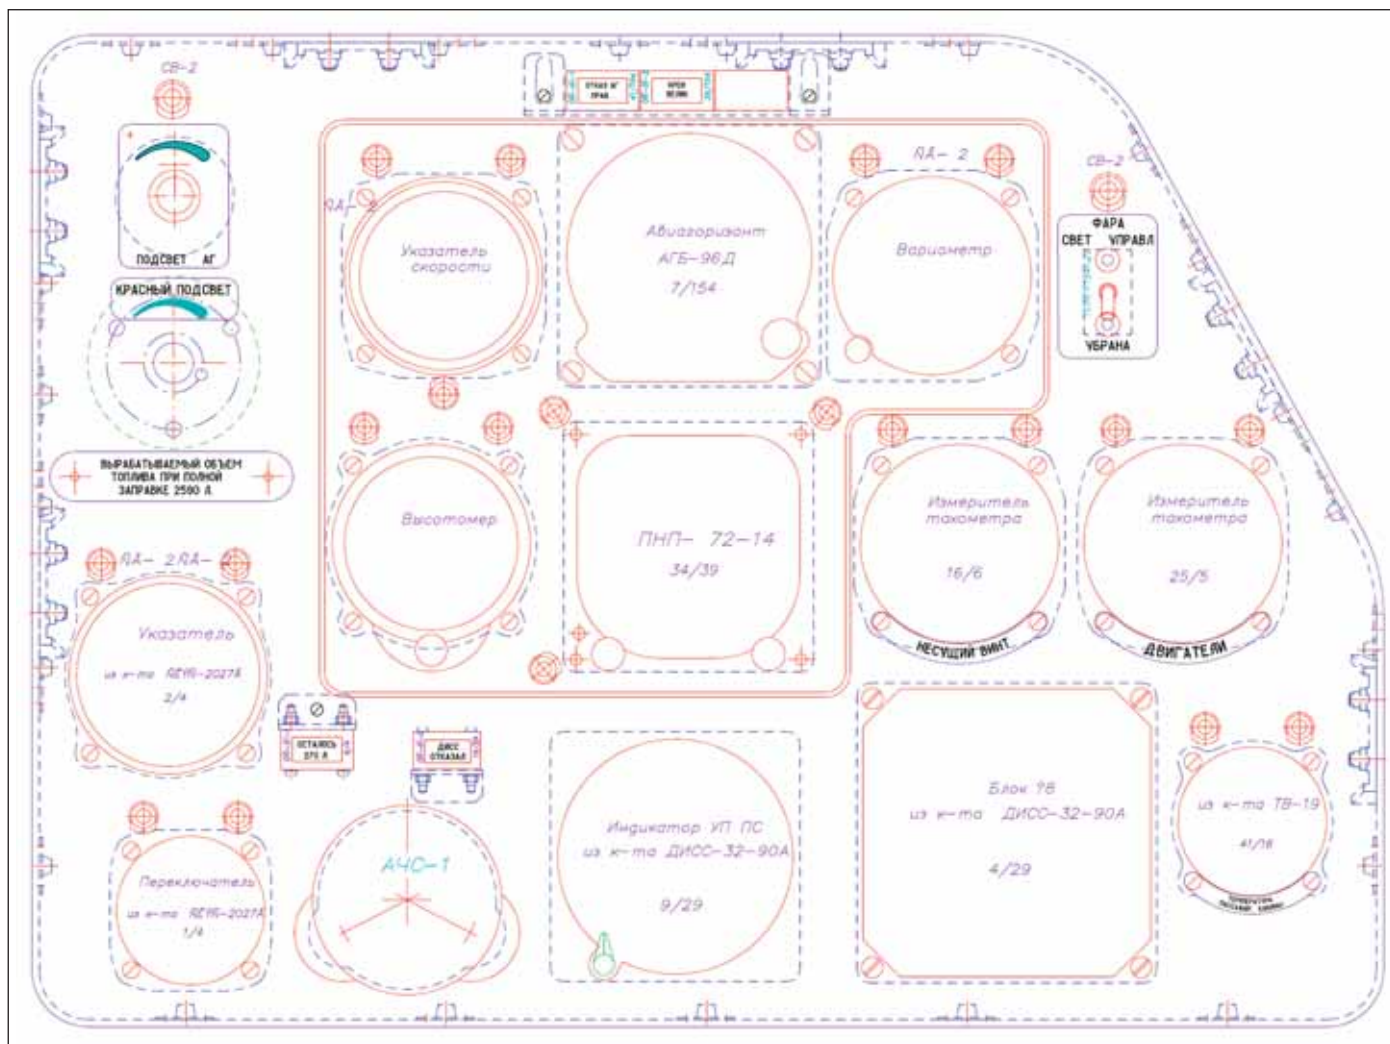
Пример чертежа приборной доски, на котором все контуры являются непосредственными источниками для формирования траектории инструмента на станках с ЧПУ
